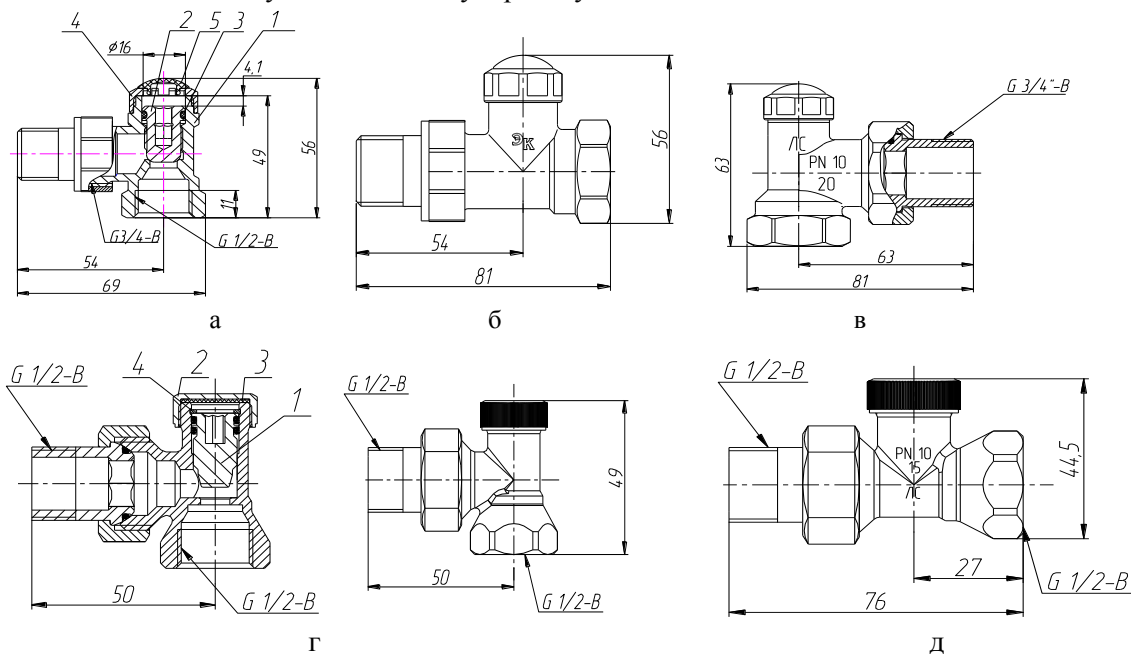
Общий вид и устройство клапанов регулирующих
